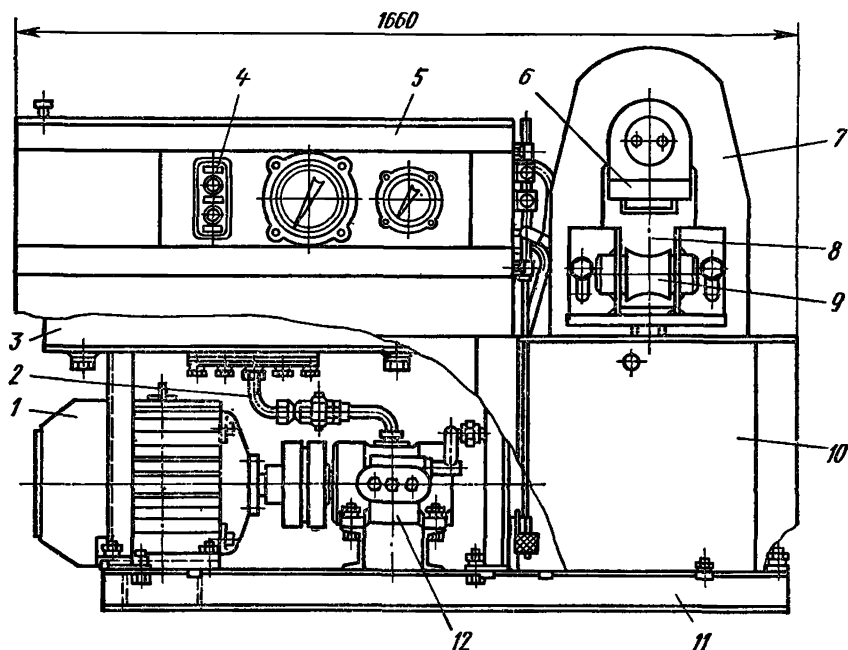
Станок СМЖ-175 для резки арматурной стали:
